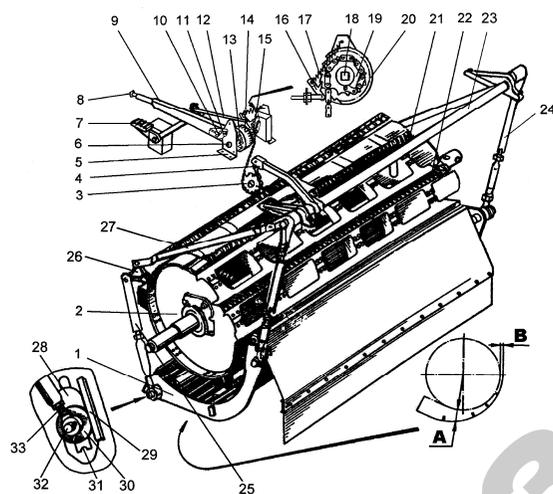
Молотильный аппарат: 1 — подбарабанье; 2 — барабан молотильный; 3, 19 — звездочки; 4 — рычаг вала торсиона; 5 — опора; 6 — вал рычага; 7 — педаль; 8 — кнопка; 9 — рычаг; 10 — ось; 11, 16 — собачки; 12 — тяга; 13, 20 — колеса храповые; 14 — барабан со шкалой; 15 — цепь втулочно-роликотая; 17 — пружина; 18 — вал; 21 — бич правый; 22 — бич левый; 23 — вал торсиона; 24 — подвеска подбарабана задняя; 25 — подвеска передняя; 26 — рычаг; 27 — подвеска верхняя; 28 — щиток; 29 — зацеп; 30 — шайба эксцентриковая; 31 — выступ фиксирующий; 32 — ось; 33 — головка подвески; А, Б — зазоры между бичами и подбарабаньем
